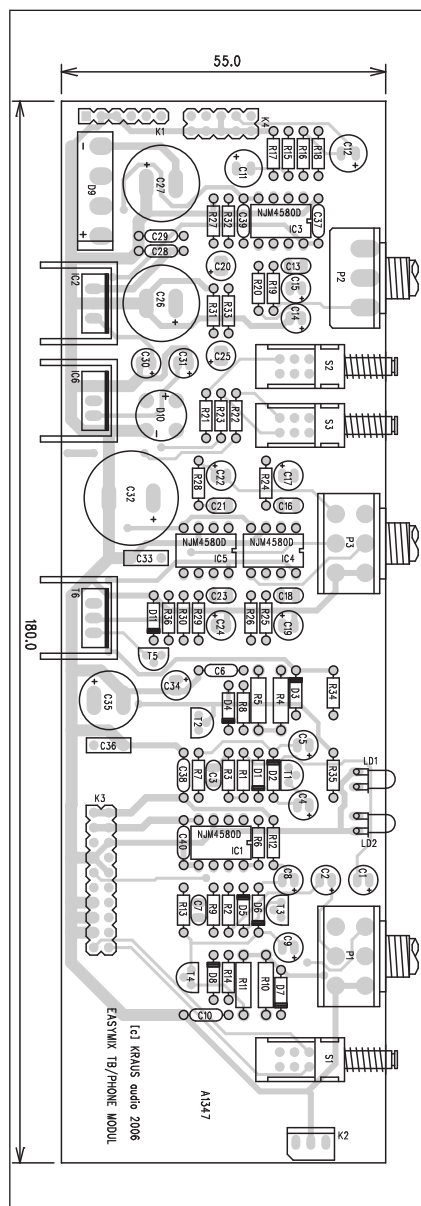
Obrazec desky spojů výstupního modulu (strana BOTTOM)
